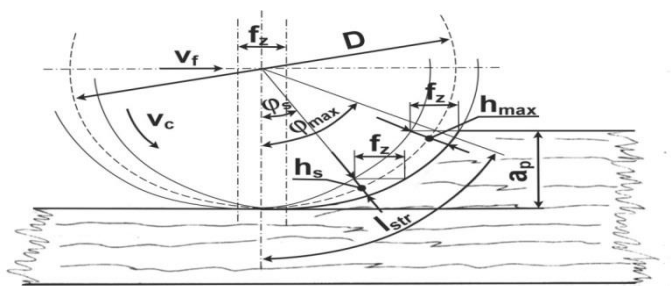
Základní typy frézování ve dřevozpracujícím průmyslu (Prokeš, 1982)
